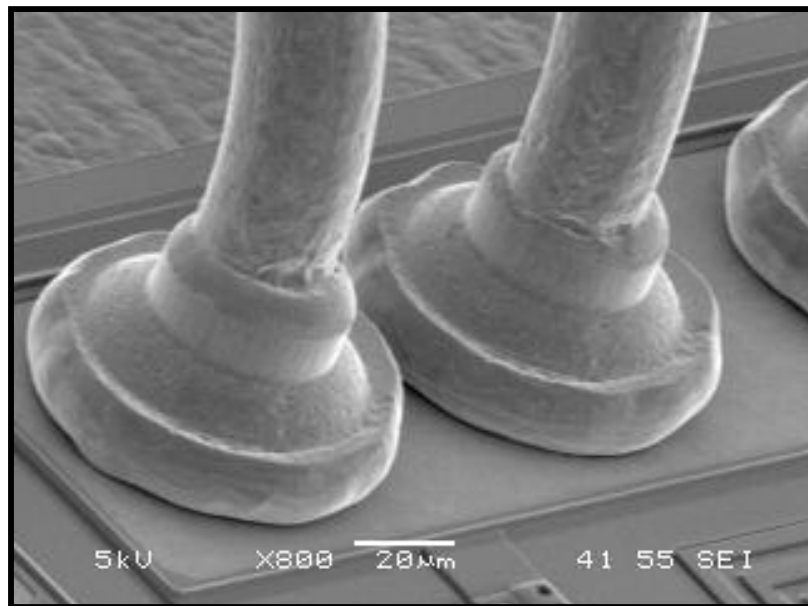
Bola de oro soldada en superficie de aluminio.
